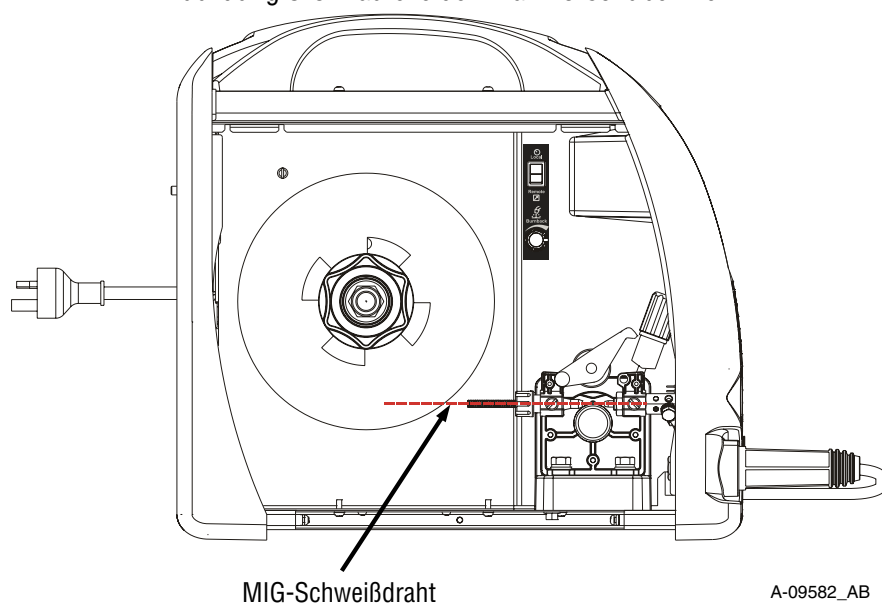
MIG-Schweißdraht - Installation
